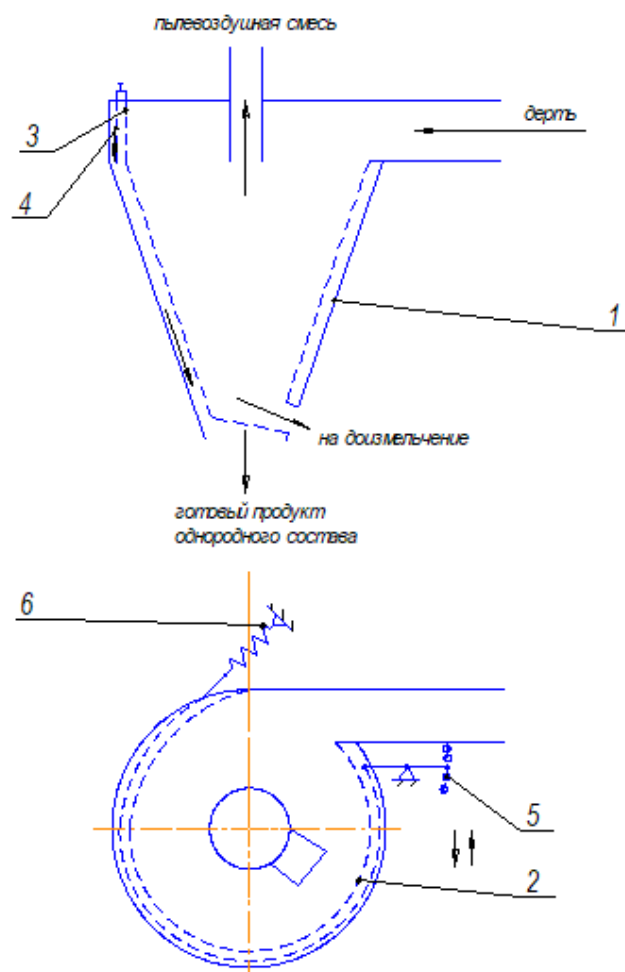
Схема сепаратора молотковой дробилки зерна с плавной регулировкой сечения отверстий
